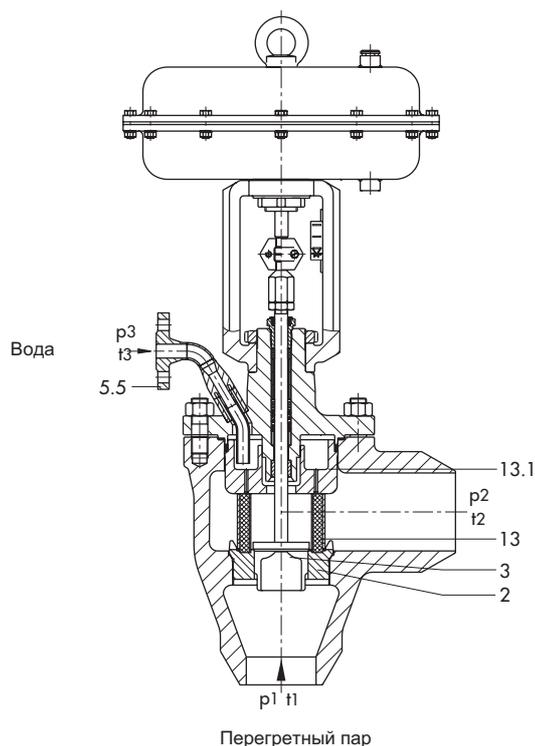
· Пневматический паропреобразователь тип 3286-1 со штуцерами под приварку и приводом тип 3271
